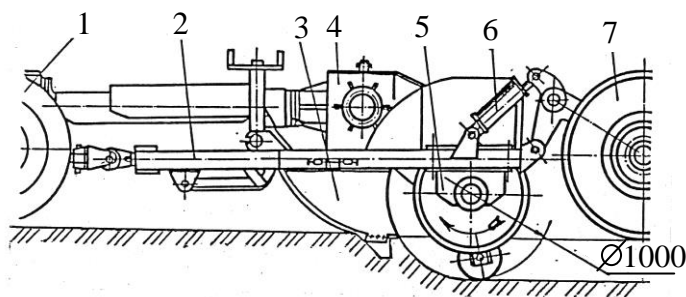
Фрезерная машина в агрегате с трактором:
